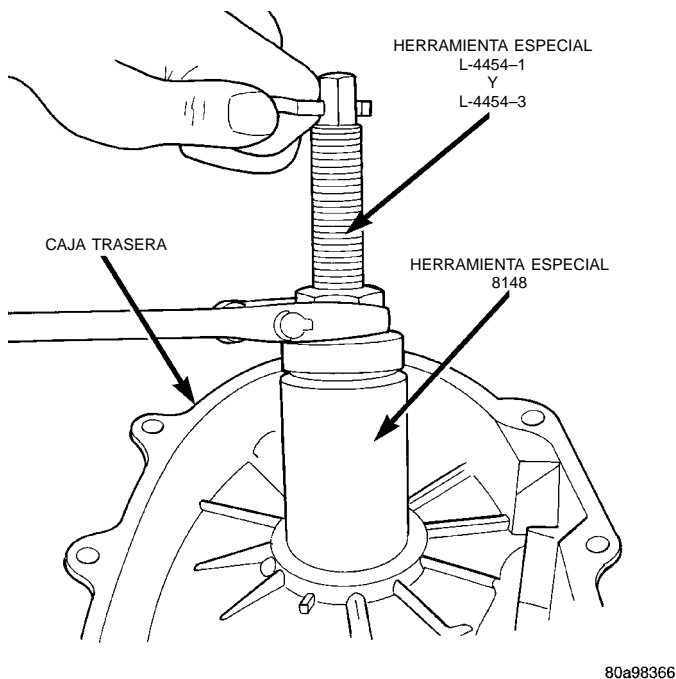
Desmontaje del cojinete trasero del eje transmisor
